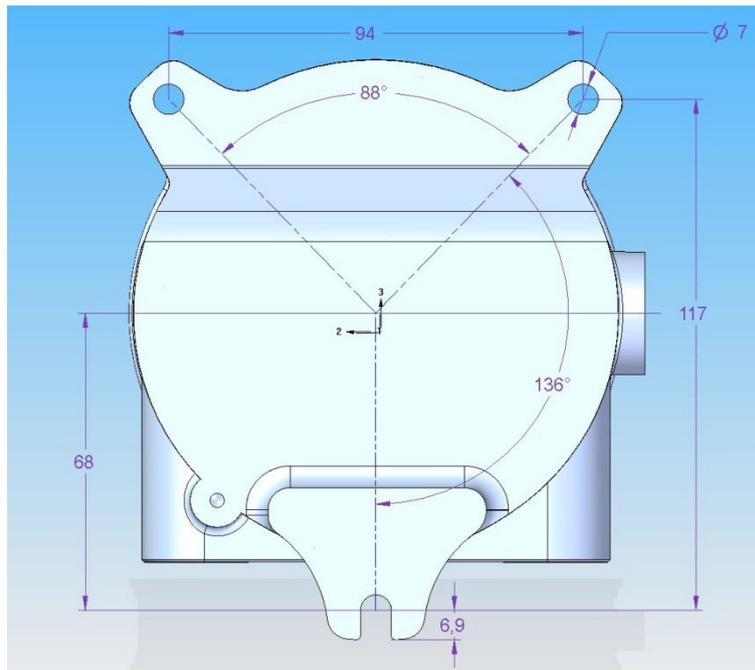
Dimensões de perfuração para fixação de suporte (mm).
